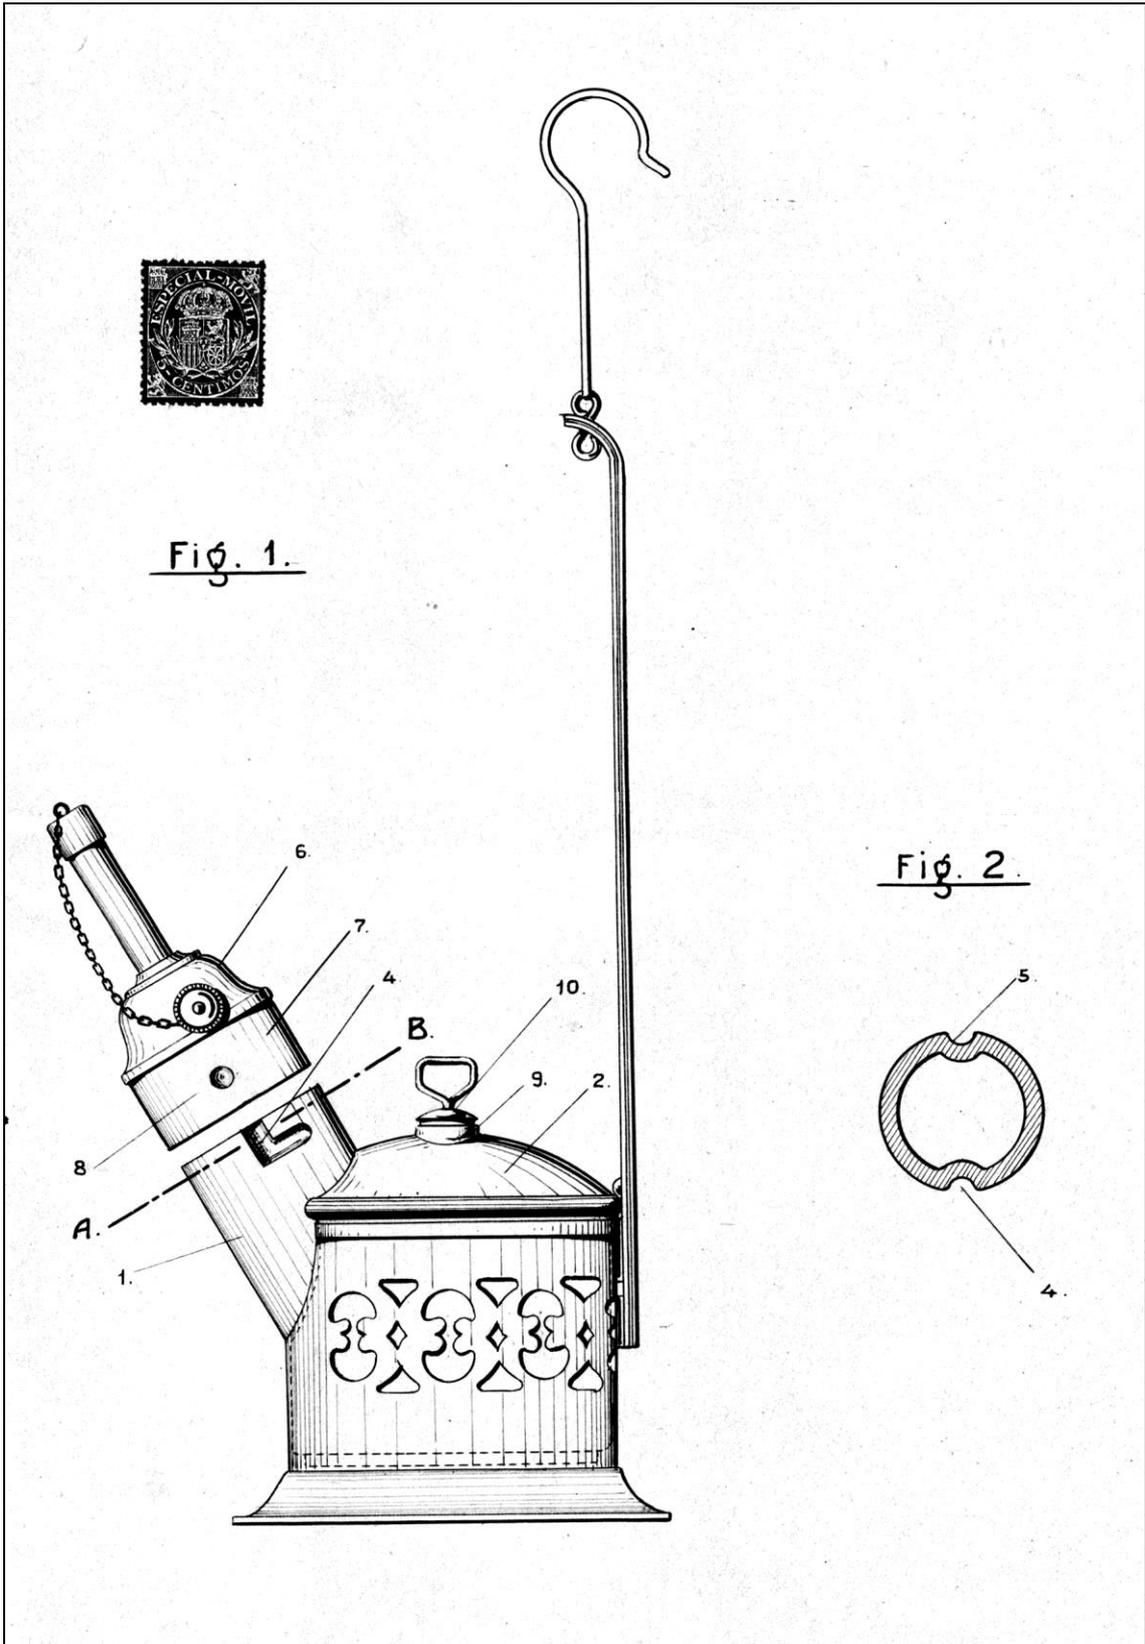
Positivo del plano de la patente (Arch.J.M. Sanchis)
